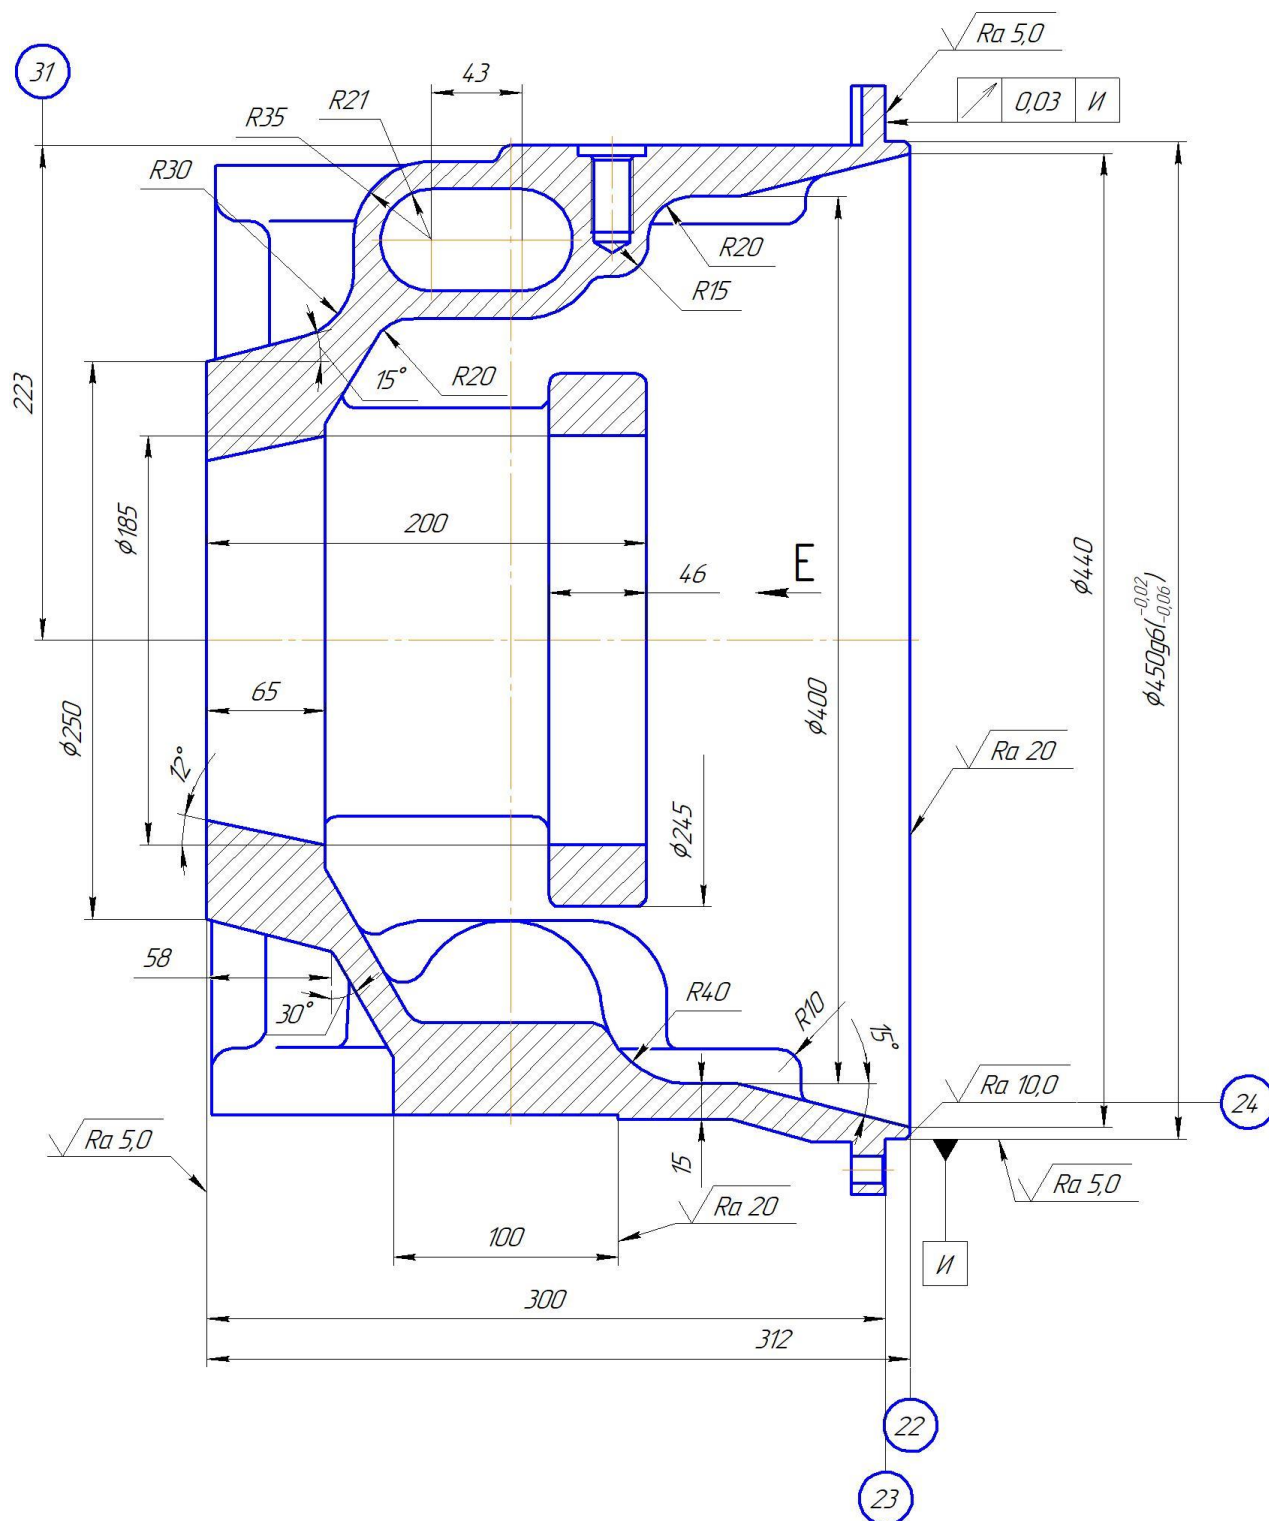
Сечение А-А. Нумерация поверхностей детали «Корпус
